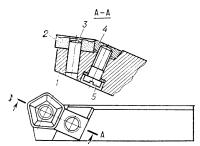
Резец с многогранной неперетачиваемой твердосплавной пластинкой: 1 — державка; 2 — пластинка; 3 — штифт; 4 — клин; 5 — винт.
